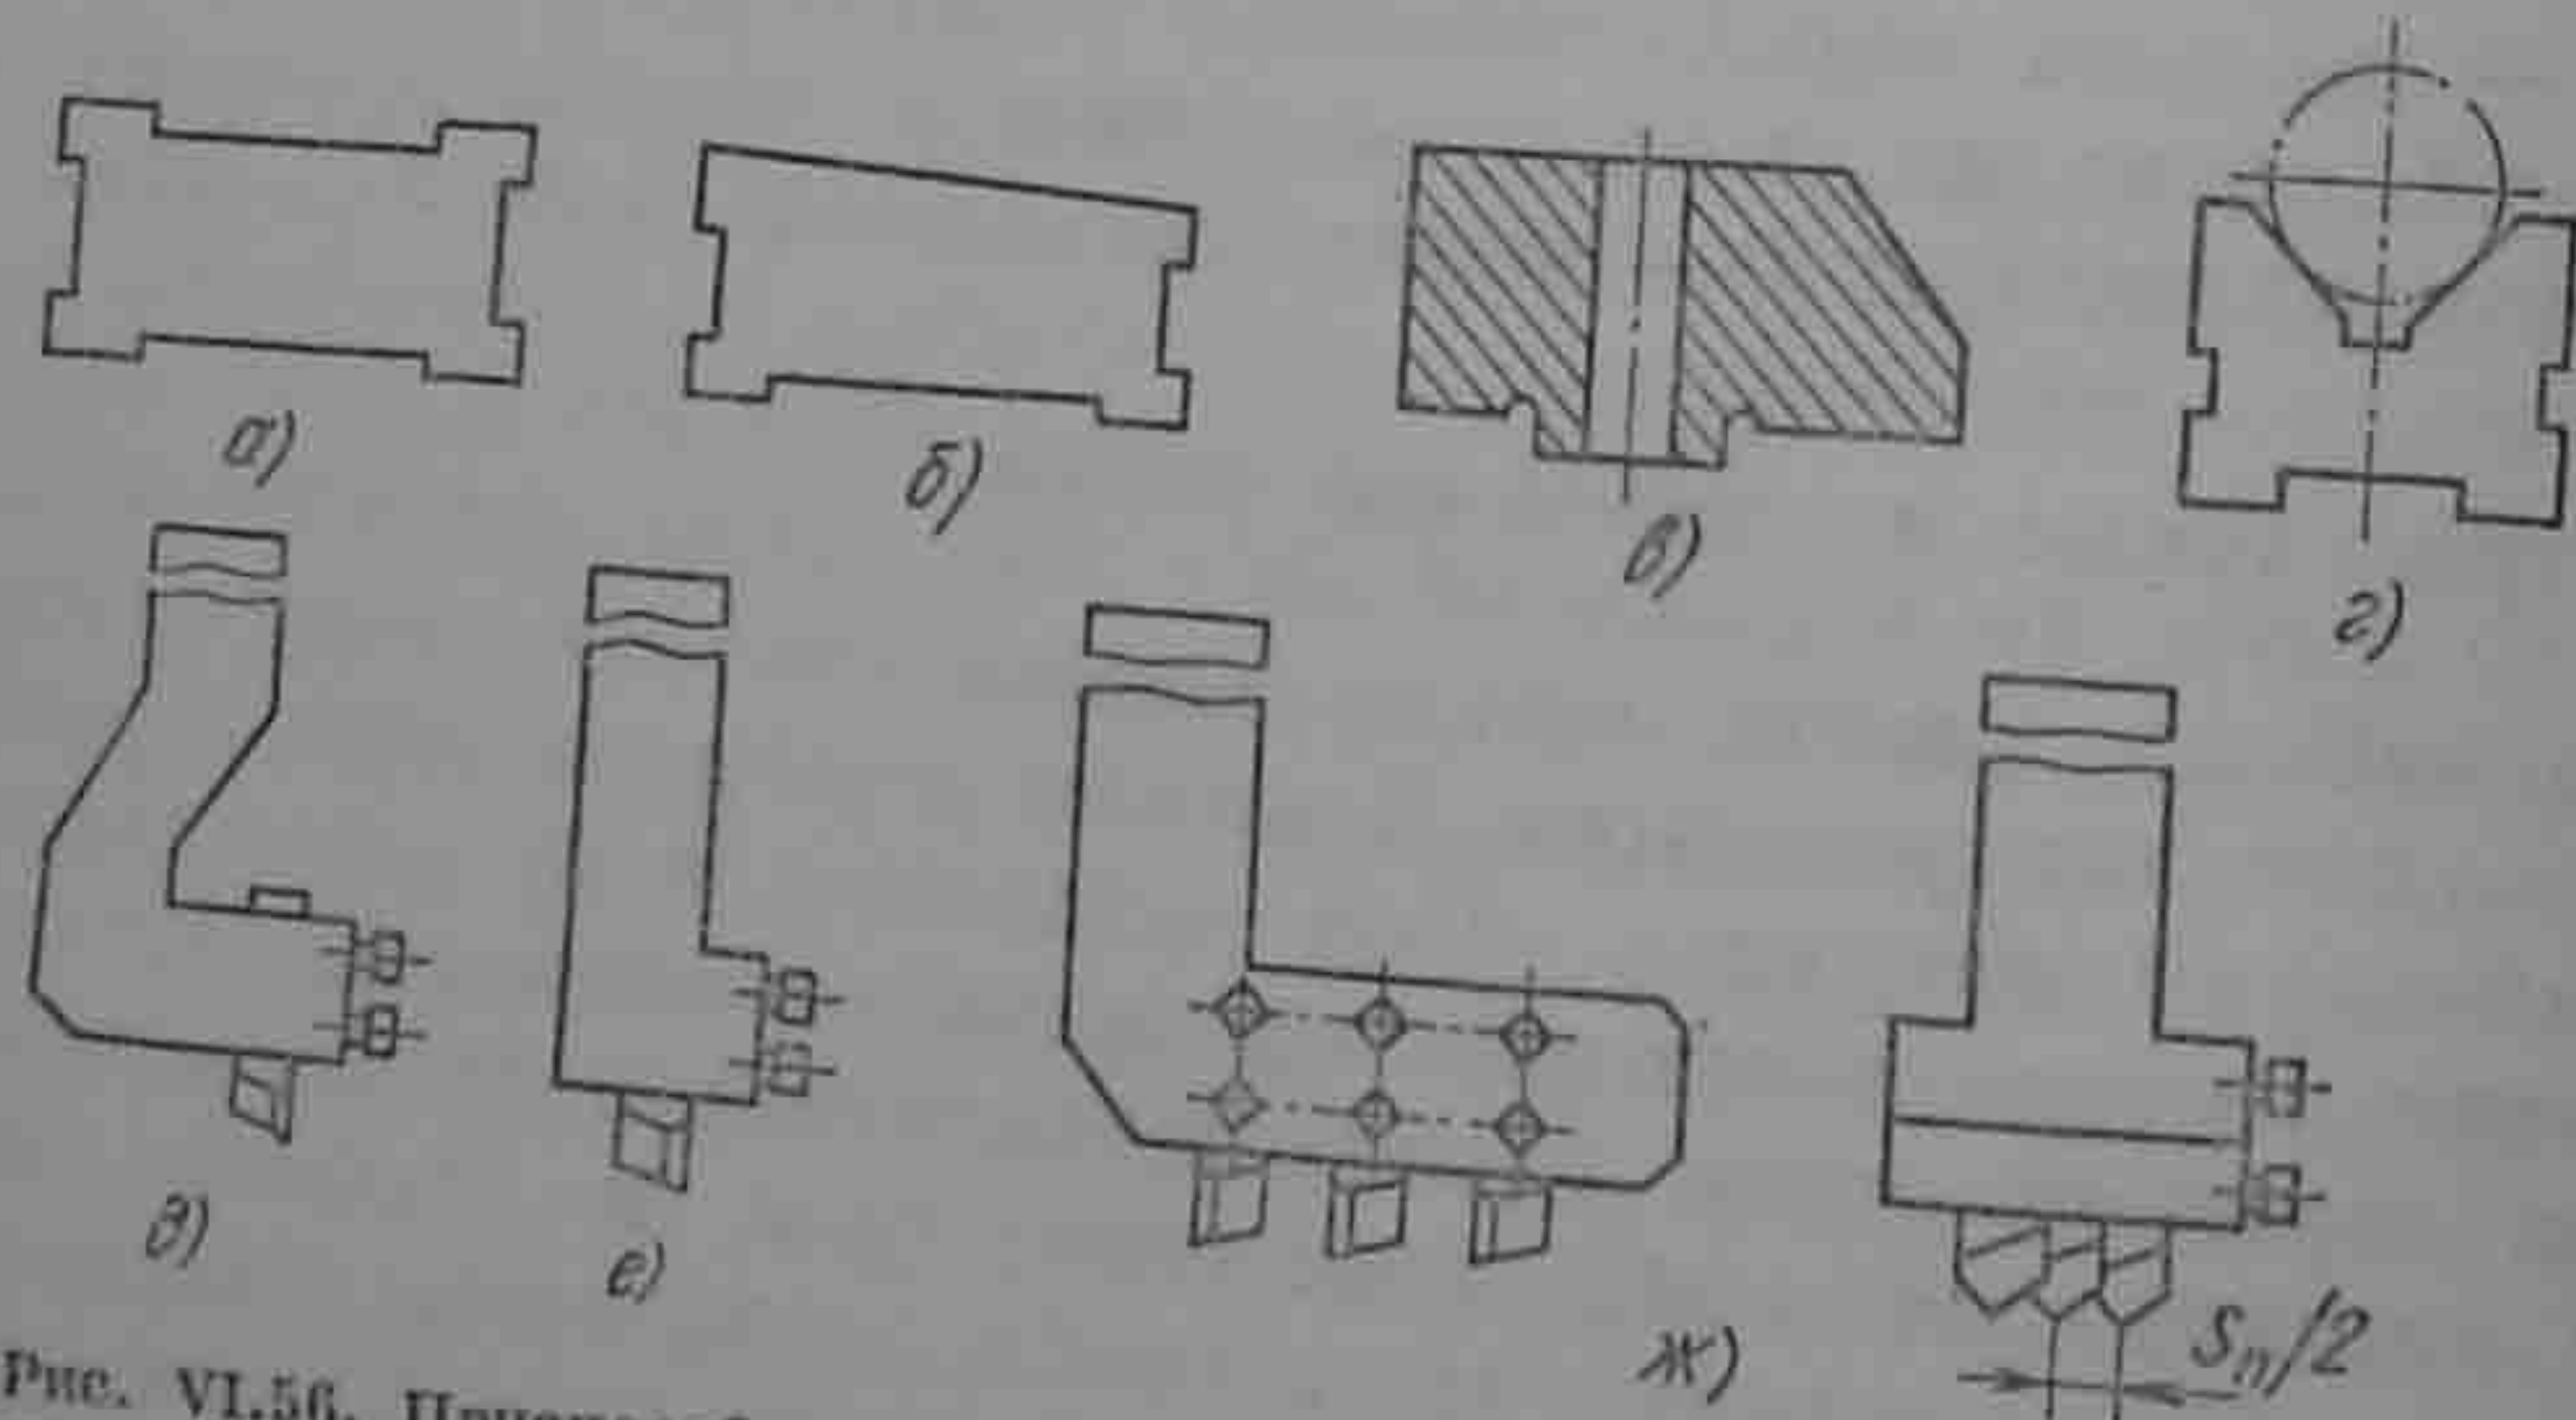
Приспособления и резцовые державки к строгальным станкам
